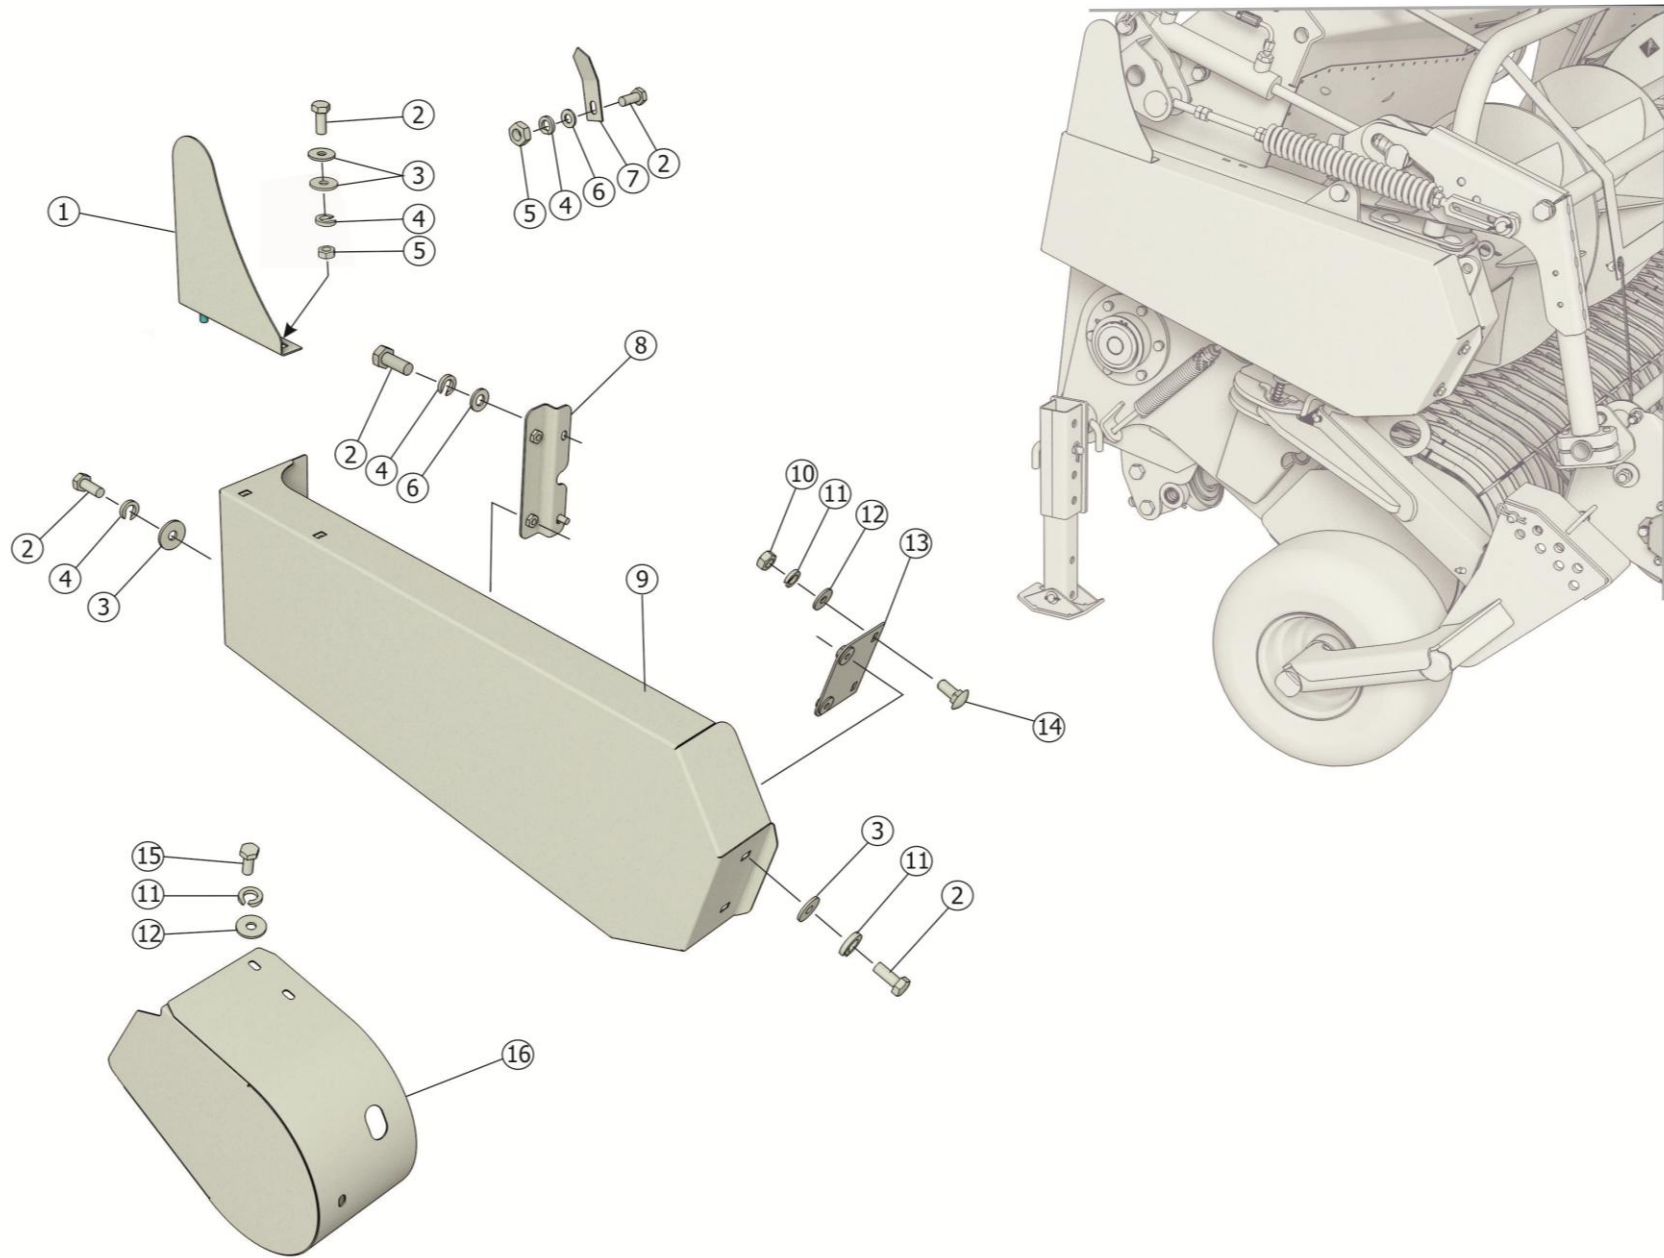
Навеска щитков ПК-300.01.11.000. Вид справа
